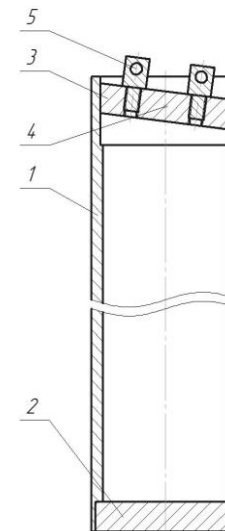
Эскиз пробоотборников типа ПО-80. 1 – корпус; 2 – донце; 3 – поворотная крышка; 4 – винты крышки; 5 – бобышка для крепления троса.
